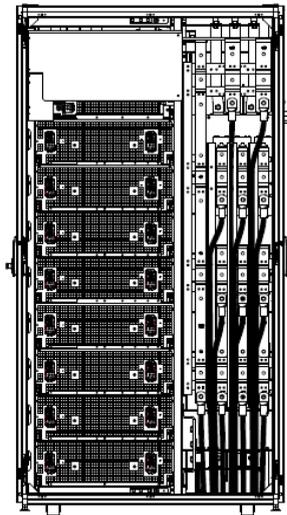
Entrada de cables para gabinete de 8 ranuras
